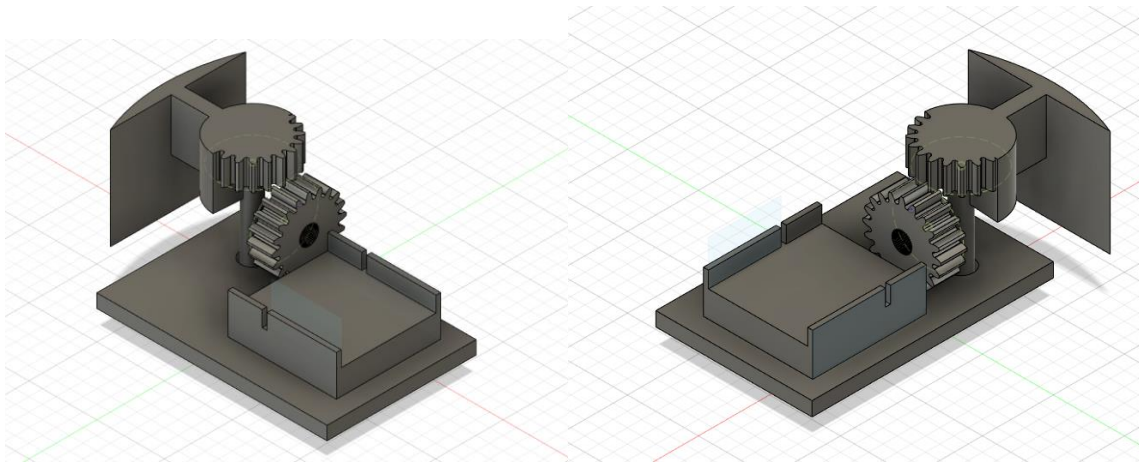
Vista isométrica de propuesta de engranaje(izquierda). Vista rotada 90° (derecha).
